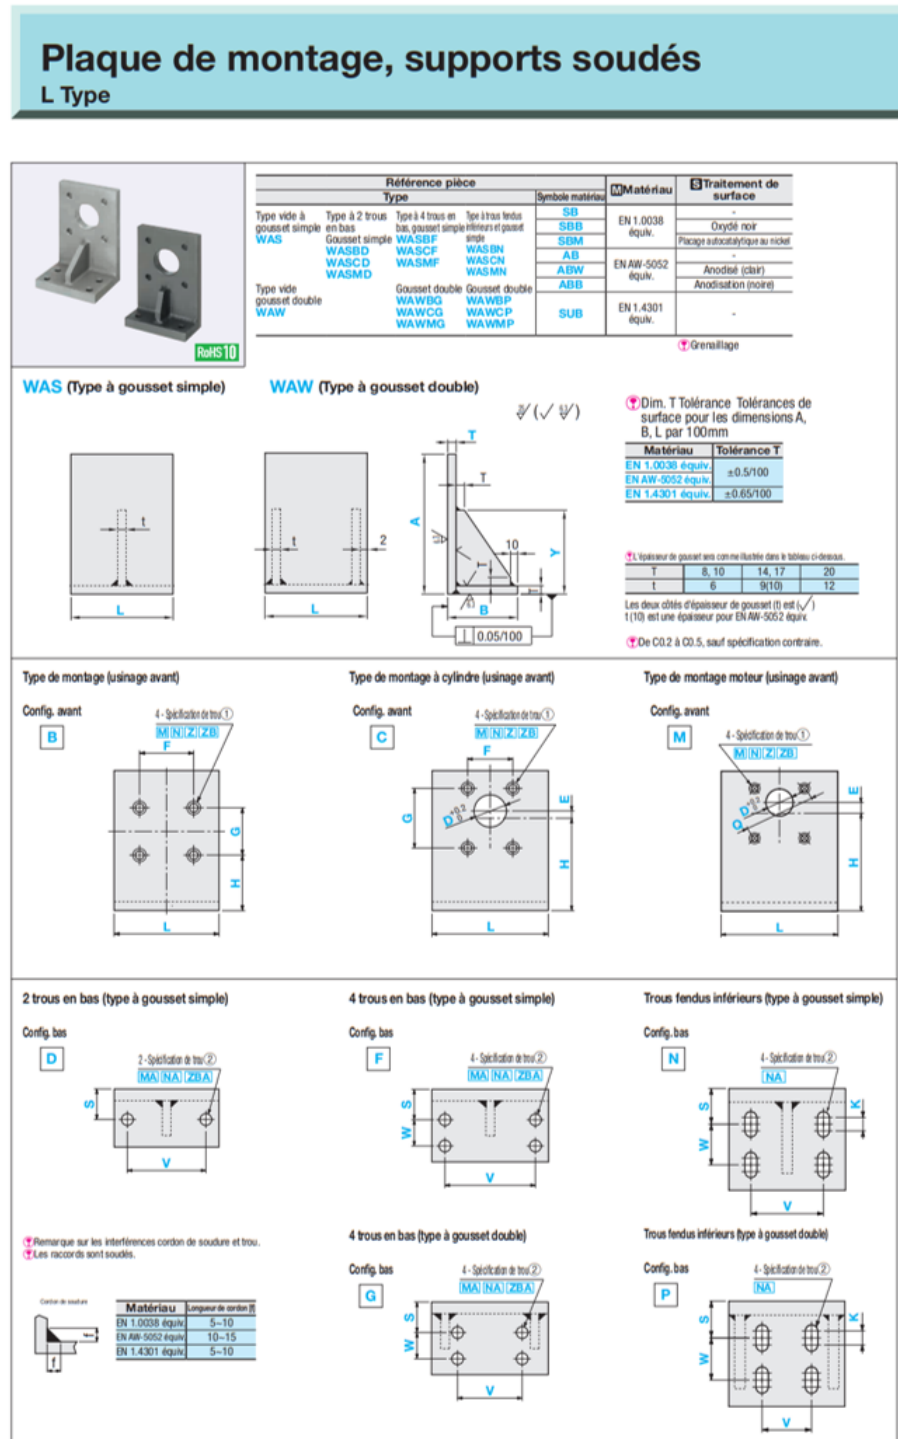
Technical drawings of the mounting bracket with reference WAWMP-ABW-T10-A160-B120-L184-Y80-H100-E0-Q120-D90-N8-V137-S60-W40-NA12-K4-CC5-RC from [25]
